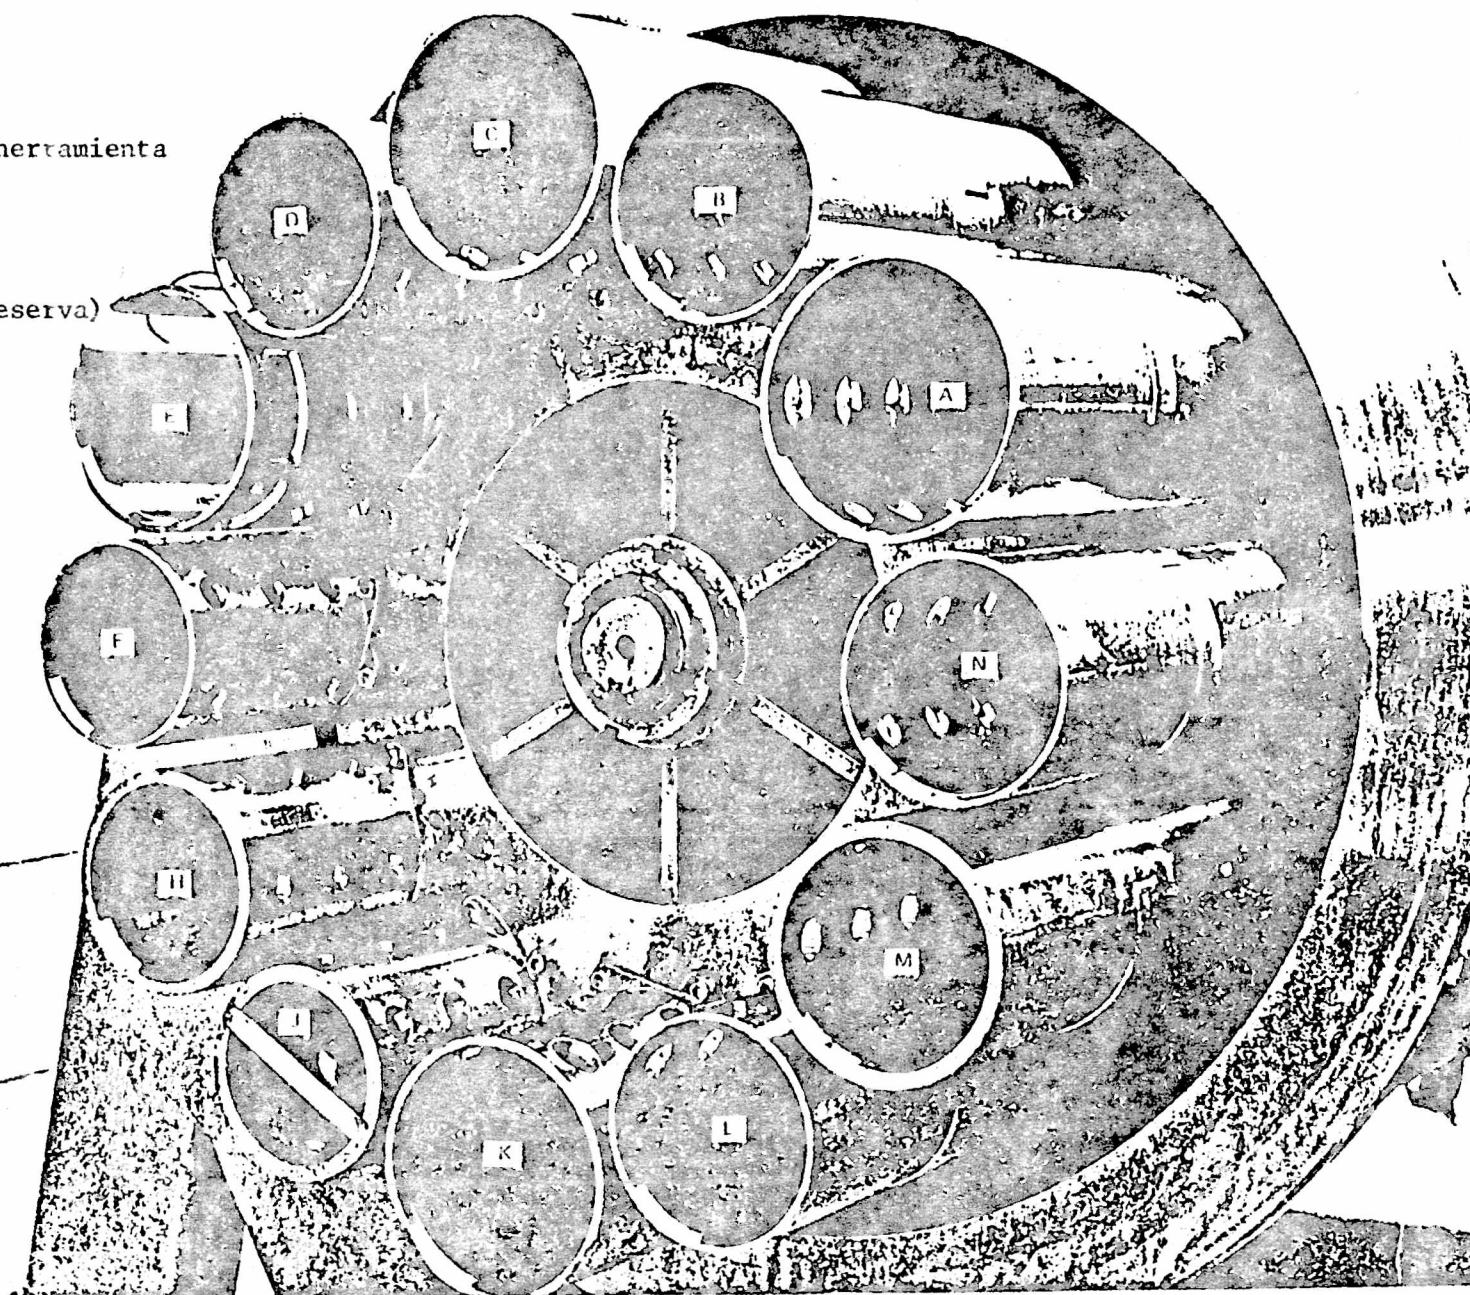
Conjunto del rotor del "Magazine" de la Máquina de Carga
